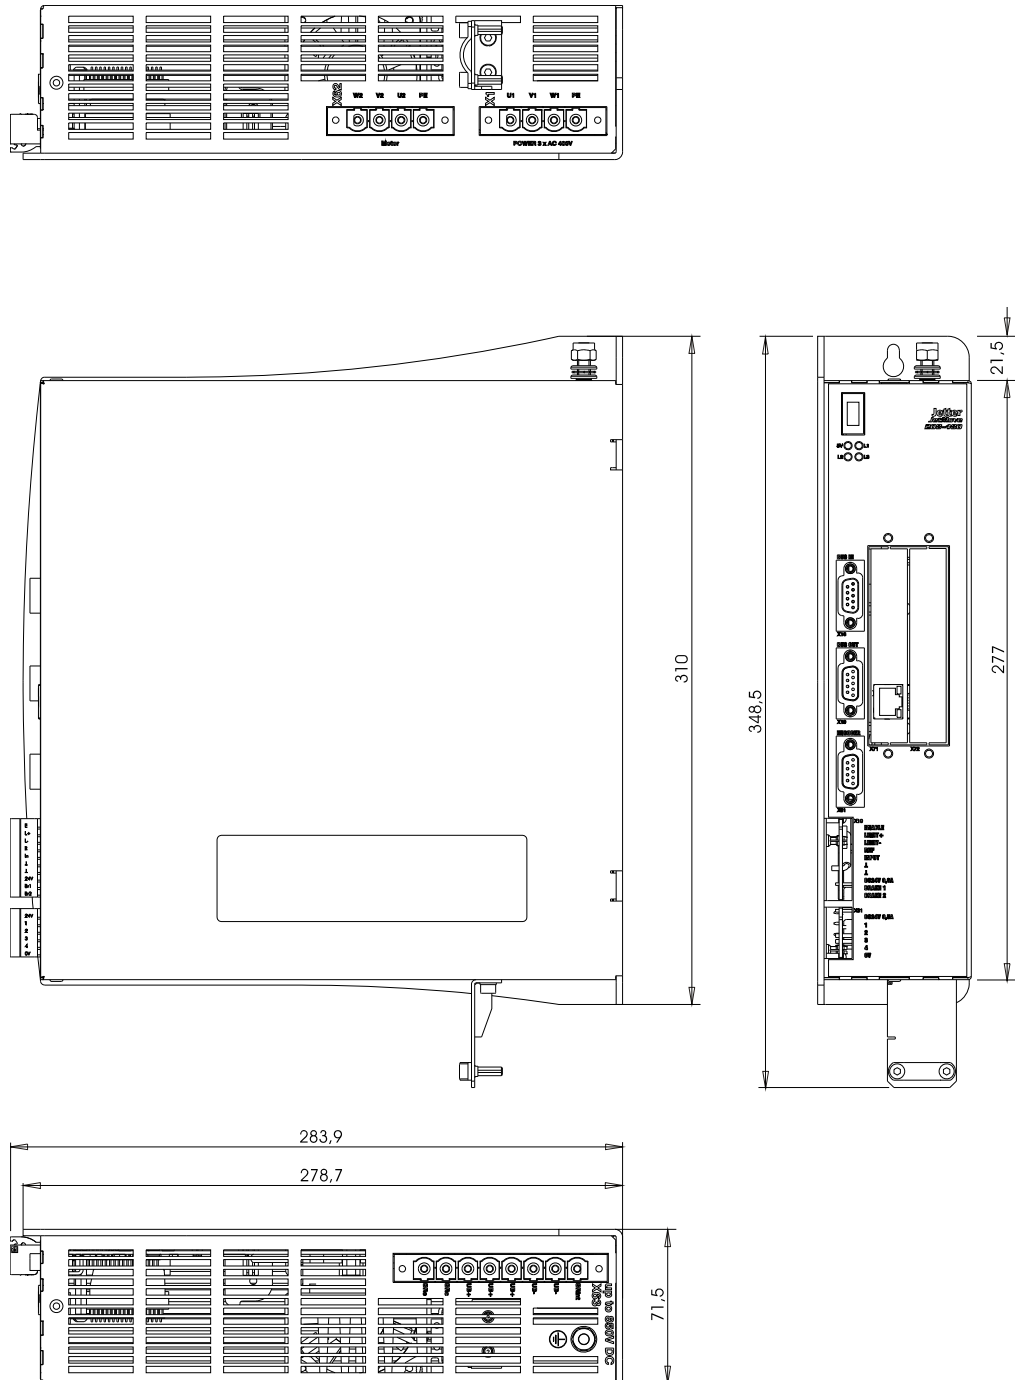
Mechanische Abmessungen JetMove 204-480 (in mm)
